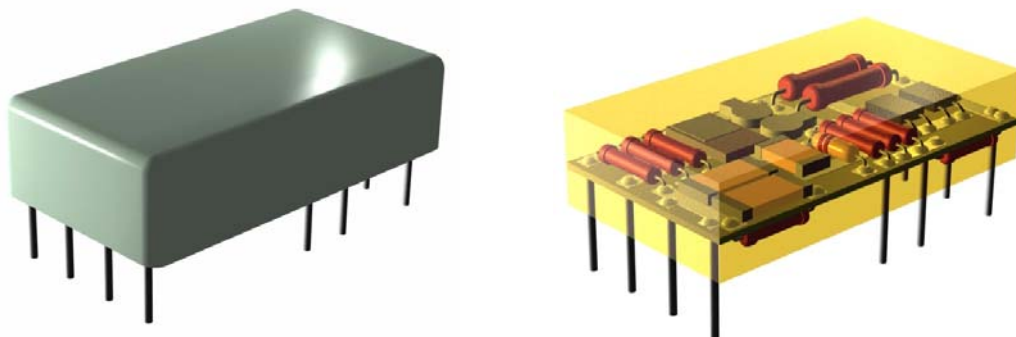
Зовнішній вигляд і конструкція типового мікромодуля
